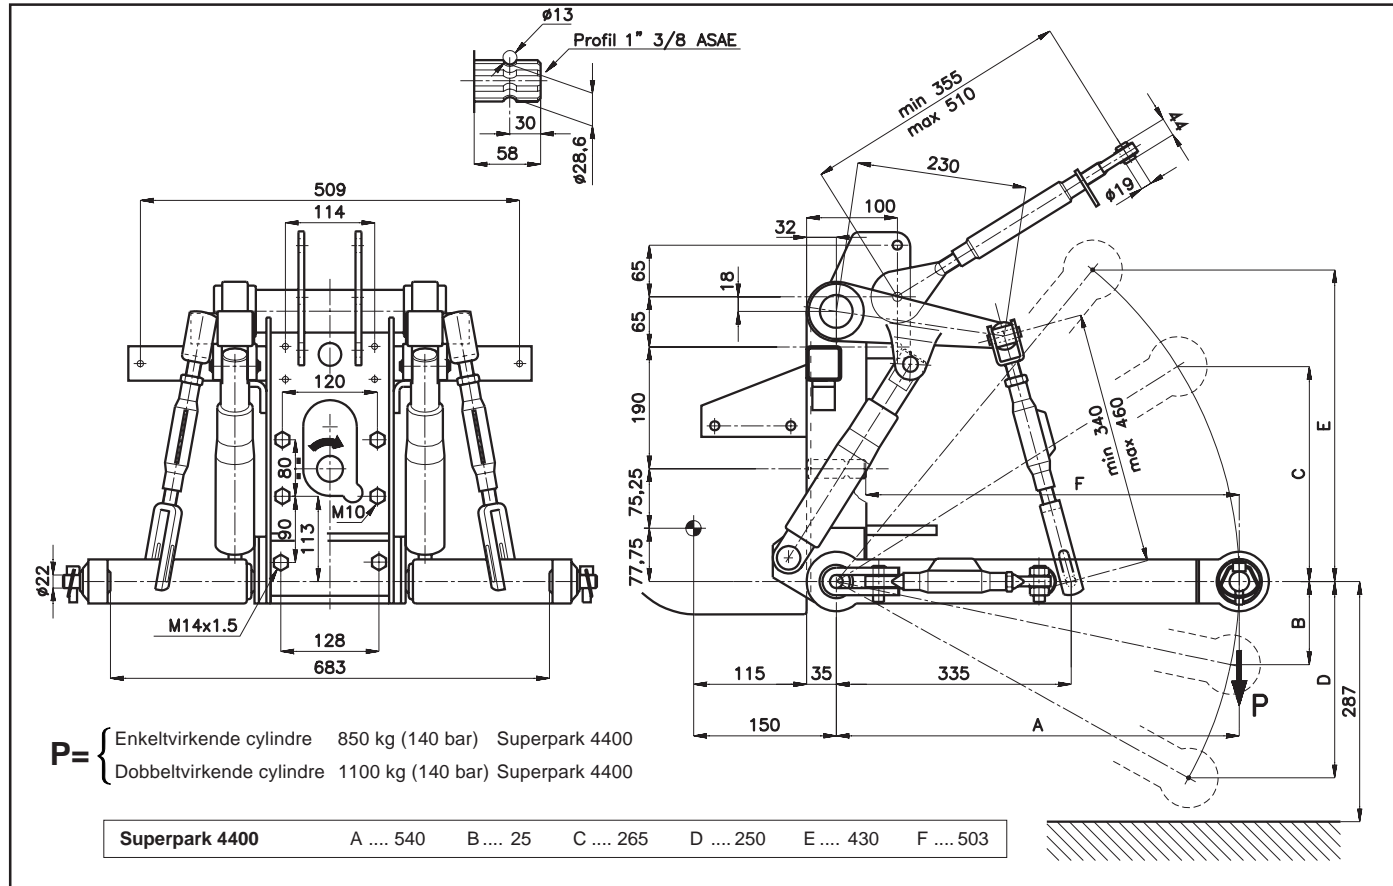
Dimensioner for trepunktskobling og flanger ved kraftudtag, med 6.50 - 16 hjul.
